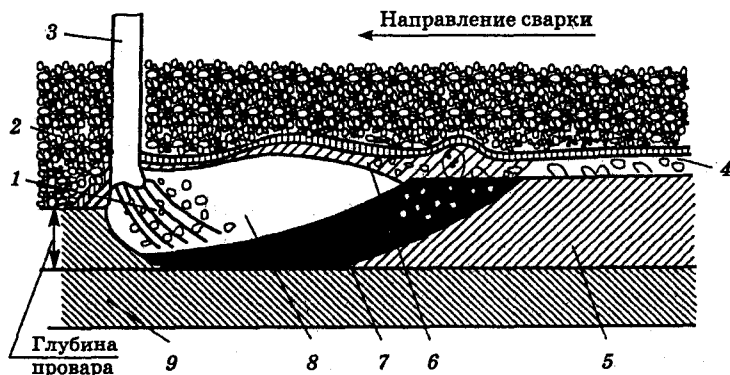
Схема процесса сварки под флюсом
